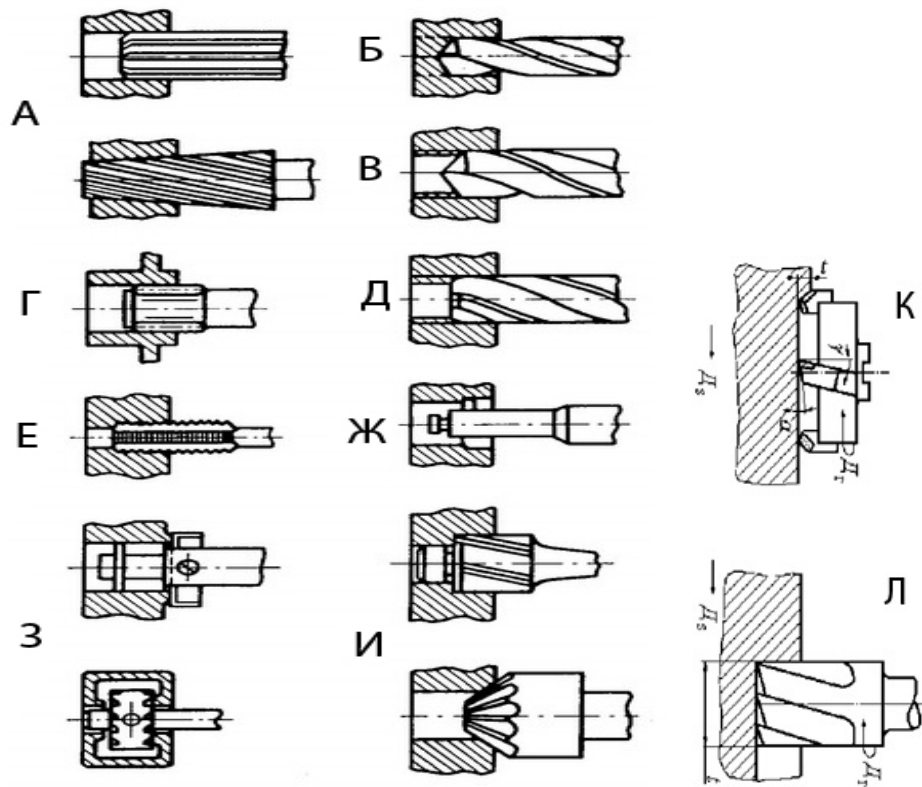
Роботи, що виконуються на свердлильно-фрезерно-розточувальних верстатах:
